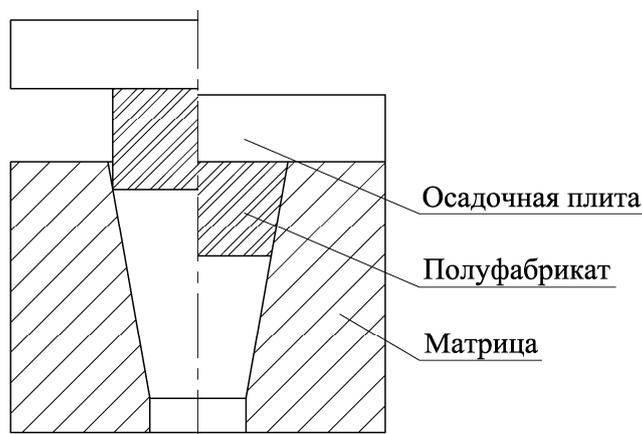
Разработанный способ получения профилированных заготовок конической формы
